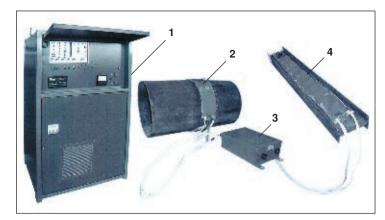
Установка ООО «НПП Курай» для подогрева при сварке труб диаметром 525–1220 мм (1 — пульт управления установки; 2 — секция индуктора на трубе; 3 — устройство для соединения секций индукторов; 4 — резервная секция индуктора)
